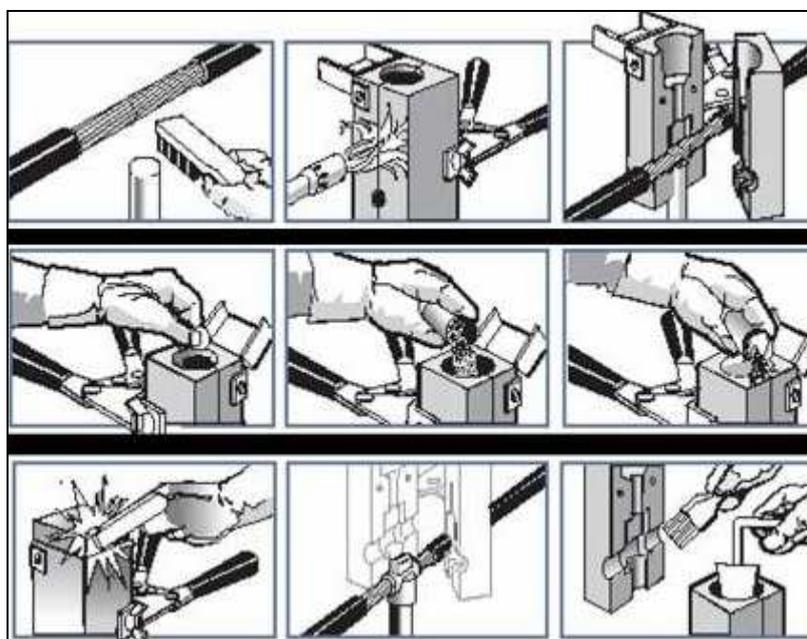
Proceso para realizar soldadura exotérmica
